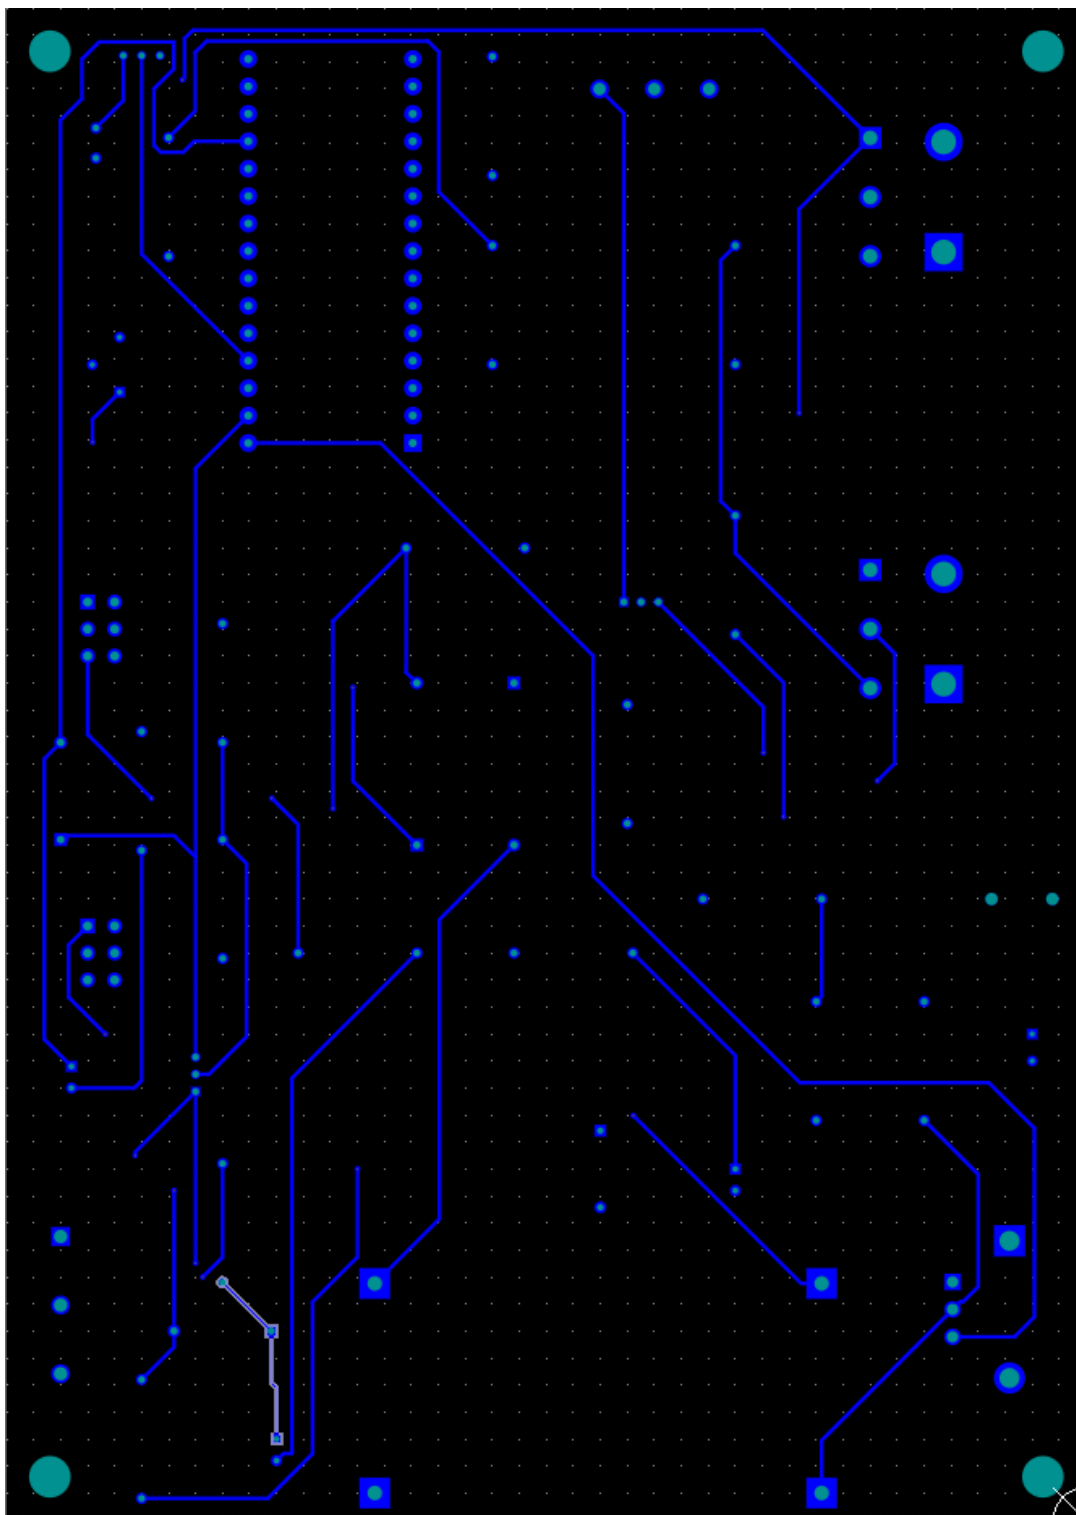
друкована плата робоча частина, шар Bottom
